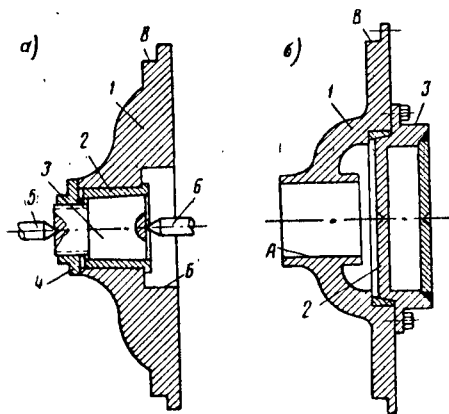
Приспособление для центровки подшипникового щита на токарном станке при расточке по двум посадочным поверхностям:
